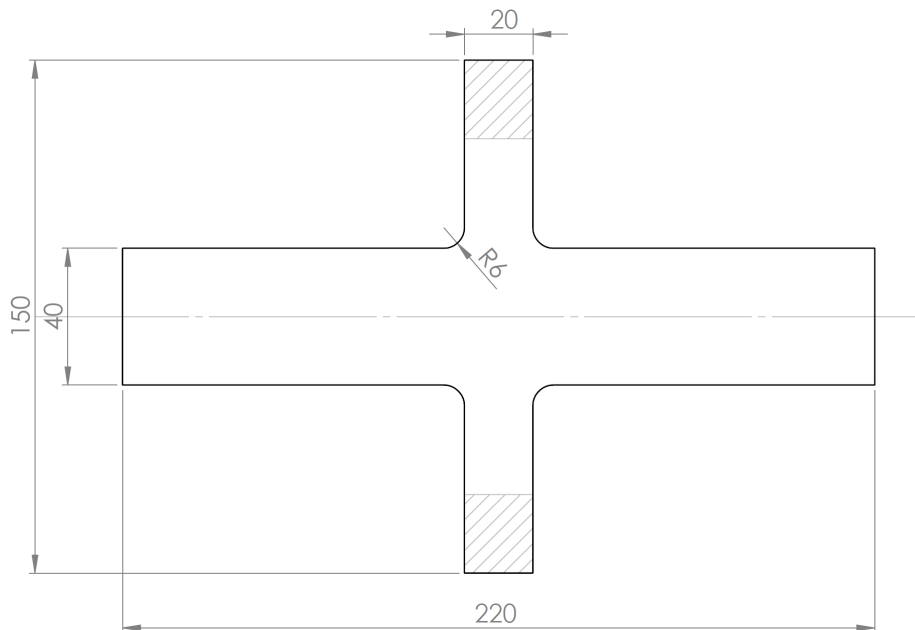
Géométrie des éprouvettes CRW (mm)
